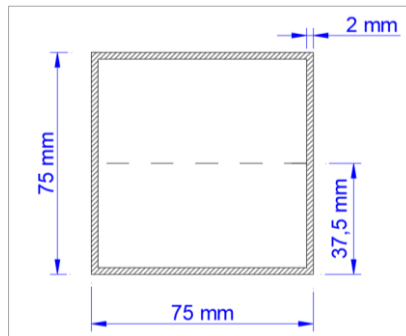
Sección transversal del tubo empleado para la construcción del brazo.
